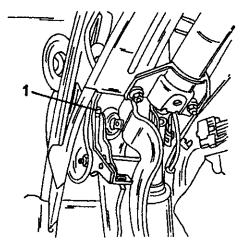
Для регулировки педали сцепления на двигателях типа XU отвернуть и снова затянуть болт (1) (см. текст).
